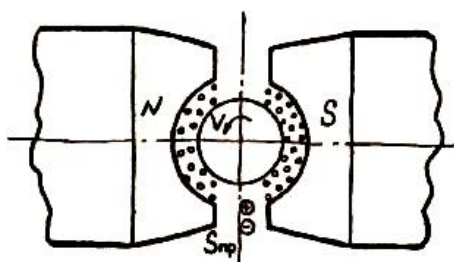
Схема обробки циліндричної заготовки в магнітному полі
